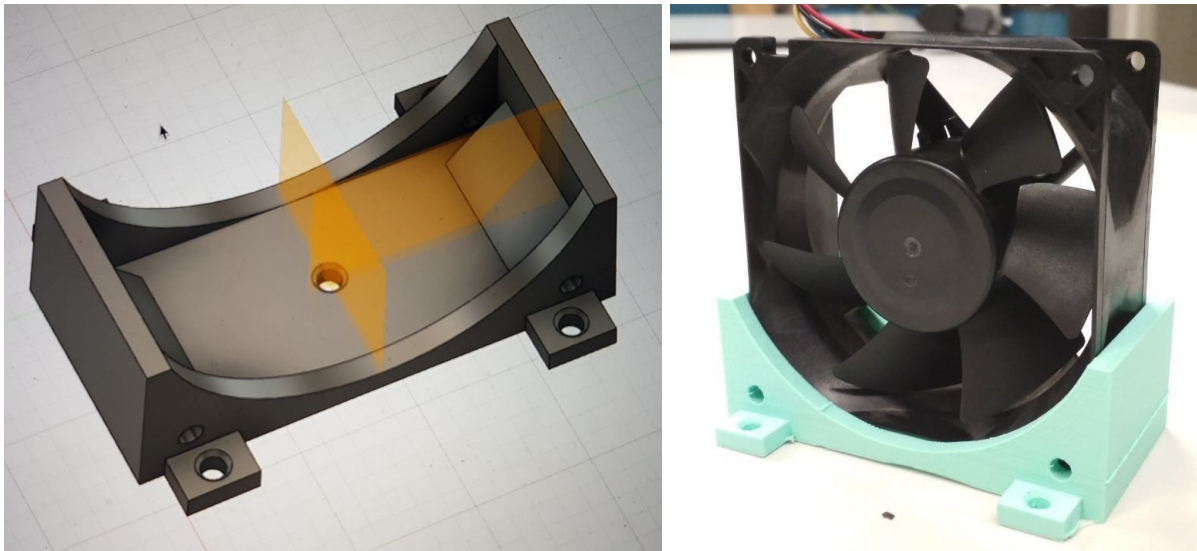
Halterung für die Lüfter. CAD Model (links) und 3D gedruckt (rechts). Die Lüfter werden von oben hineingesteckt und können optional an den Ecken befestigt werden. Die Halterung wird mit vier Schrauben auf dem Aufbau befestigt.
